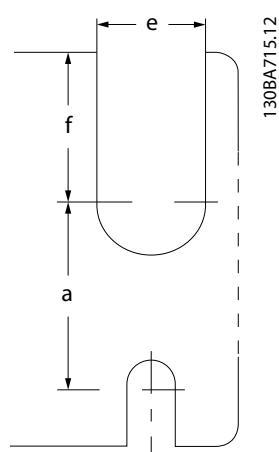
Pravilna montaža z zadnjo ploščo
